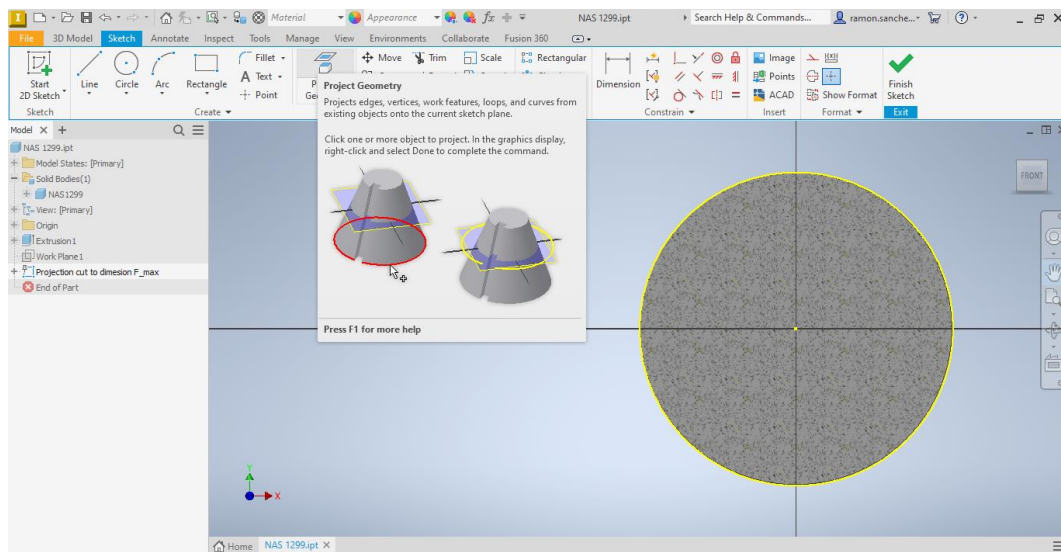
Proyección de geometría en el plano de trabajo 1
